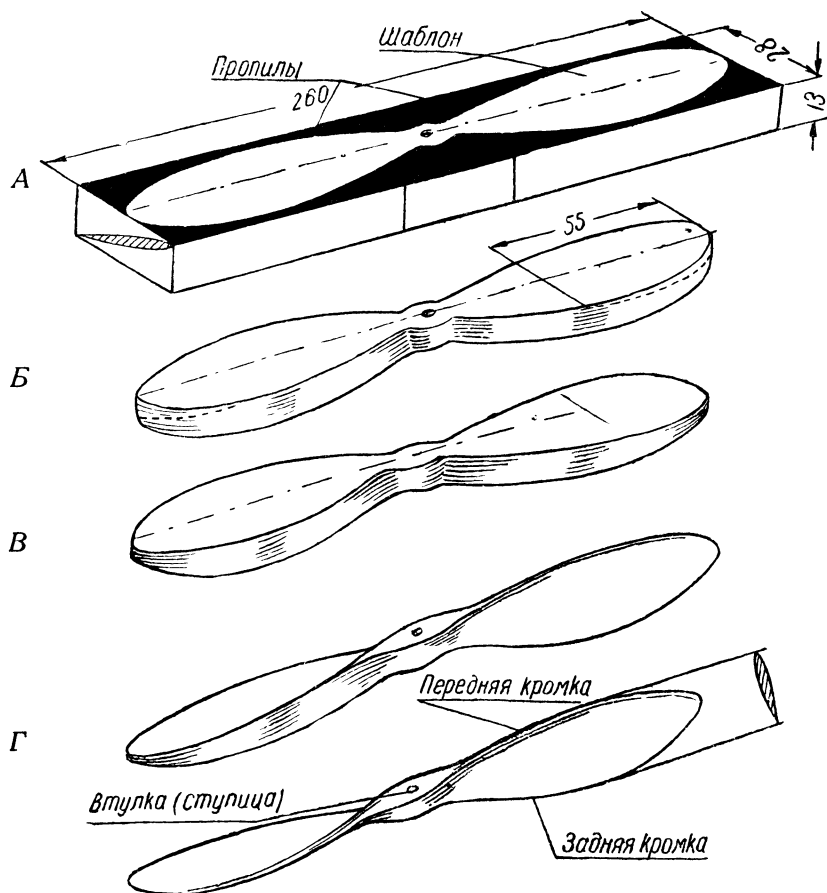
Процесс изготовления винта: А — расчерченная заготовка; Б — вырезание по шаблону; В и Г — изготовление лопасти винта; Д — общий вид готового винта
